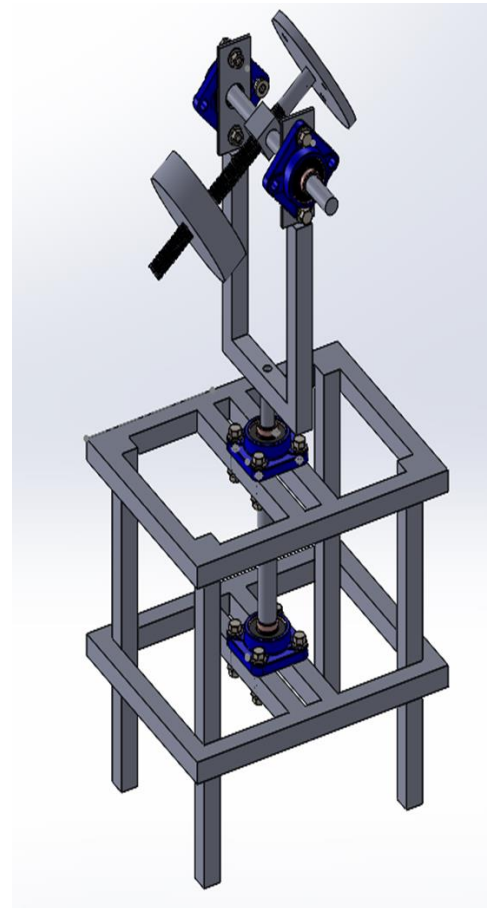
Diseño CAD de base mecánica. Fuente: Propia
